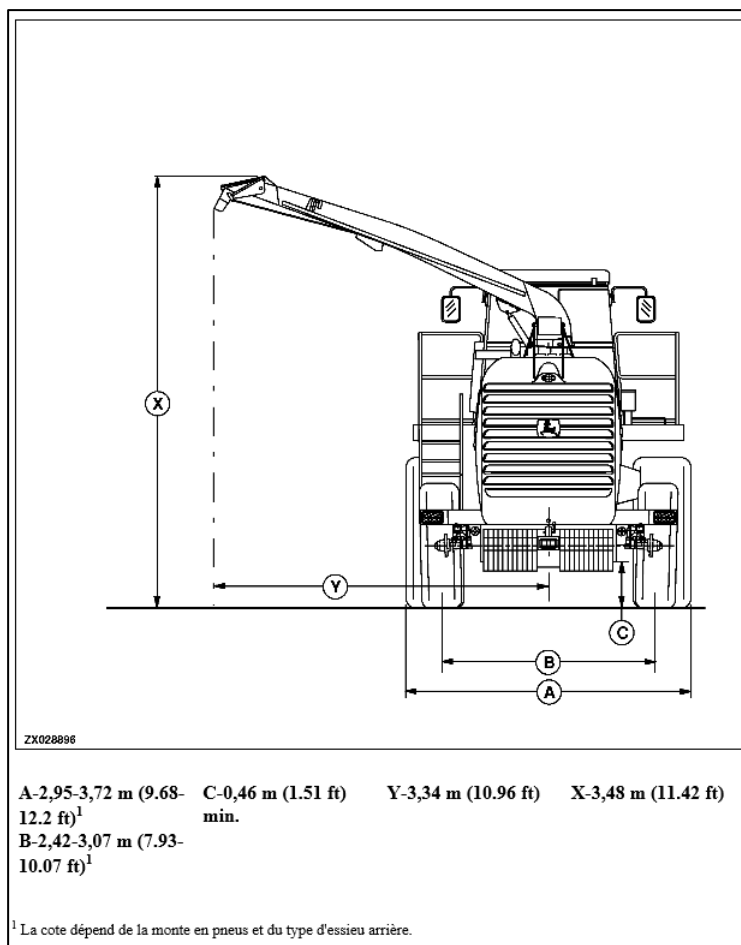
Dimensions des fourragères John Deere, modèles 7200, 7300, 7400, 7500, 7700 et 7800. Vue de derrière.
